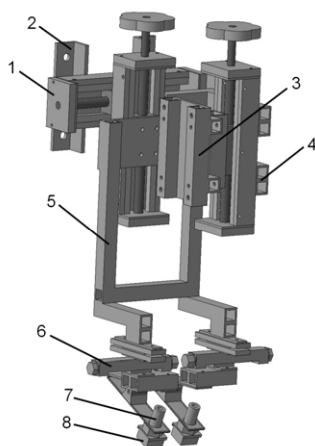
Конструкция сварочной головки: 1 – каретка сварочного портала; 2 – угловое крепление; 3 – узел для крепления сварочной горелки; 4 – приварное крепление; 5 – кронштейн для крепления токоподводов; 6 – направляющая для перемещения контактов токоподвода; 7 – пружинный поджим; 8 – медно-графитовый токоподвод
